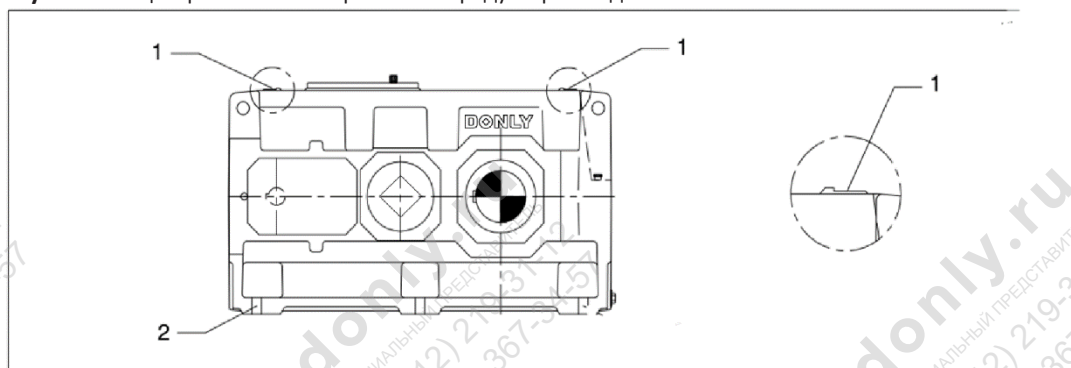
Центровочные поверхности на редукторах моделей 13–26
